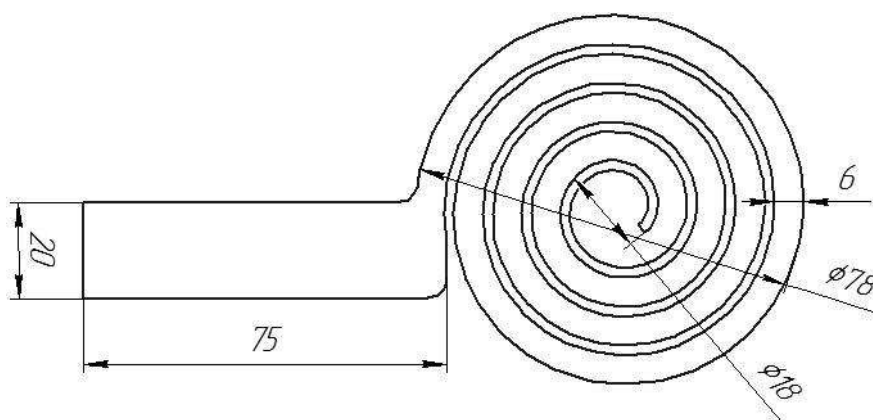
Конструкция и размеры 4х виткового индуктора
